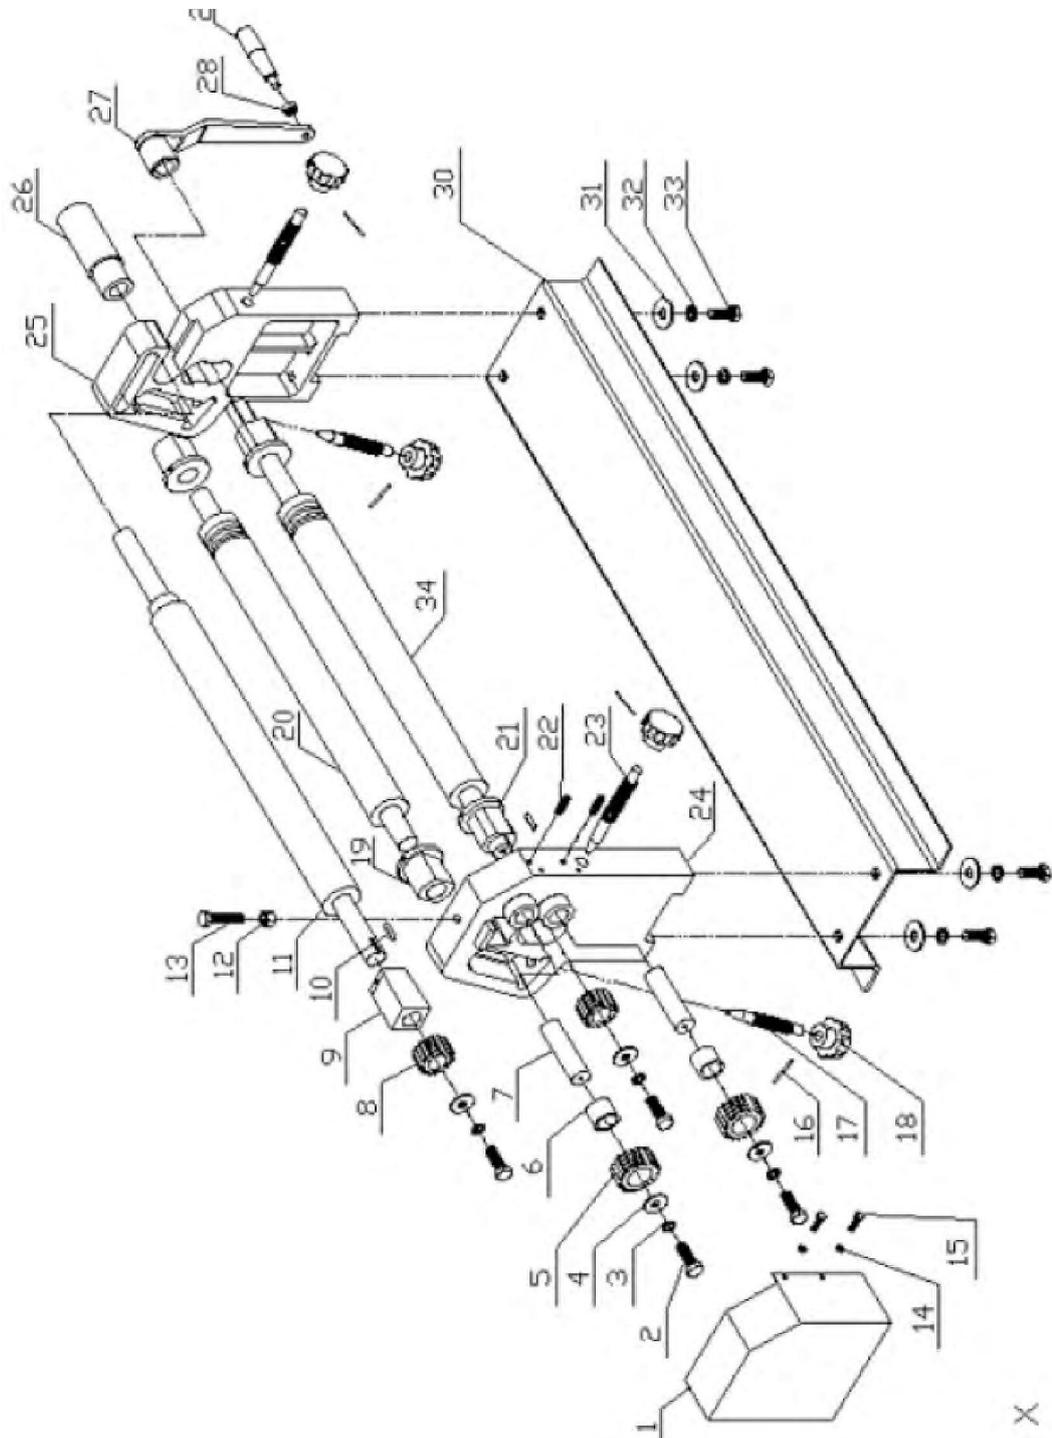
6 Piezas de repuesto - Spare parts
